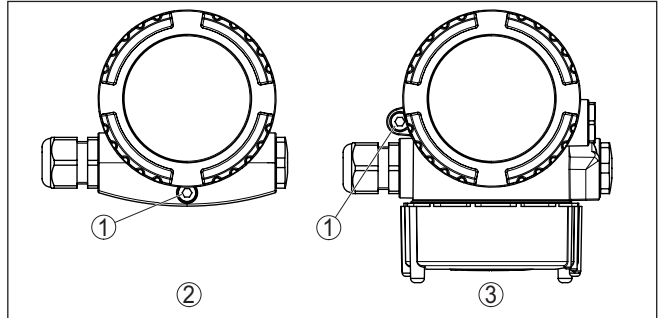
Position der Sicherungsschraube je nach Gehäuse
